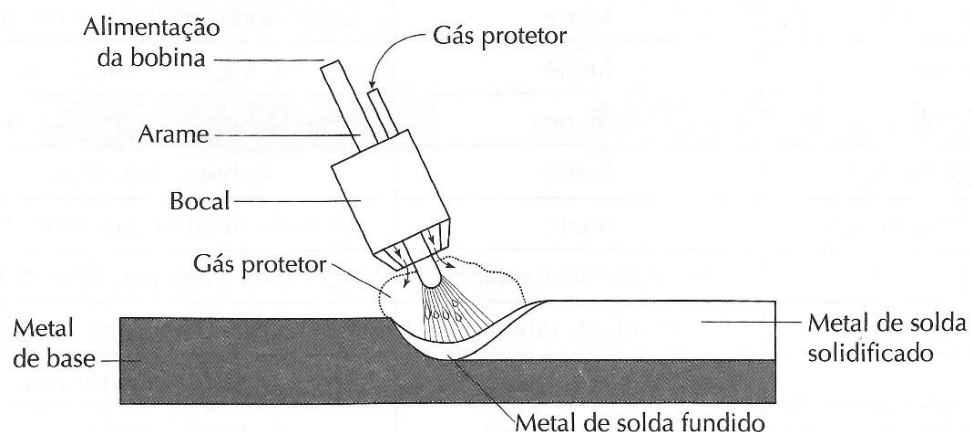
Ilustração do processo de soldagem MIG ou MAG
